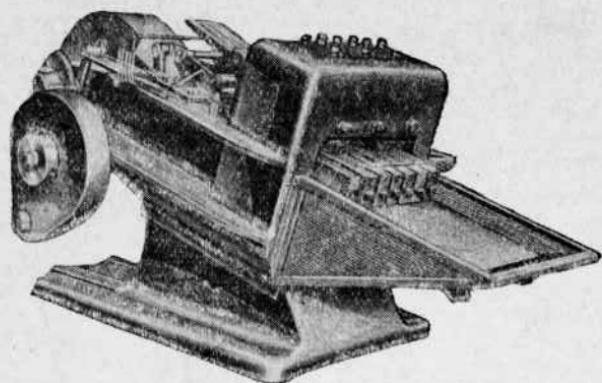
Резьбонакатный полуавтомат Ватервли-Фаррел для накатывания очень длинных деталей.
